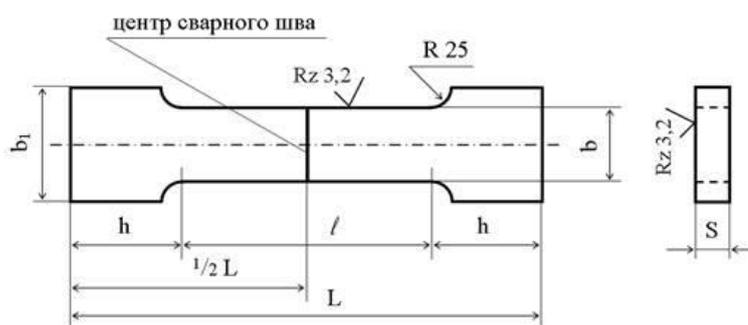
Форма образца: (тип XIII) для испытаний сварного соединения на статическое растяжение
